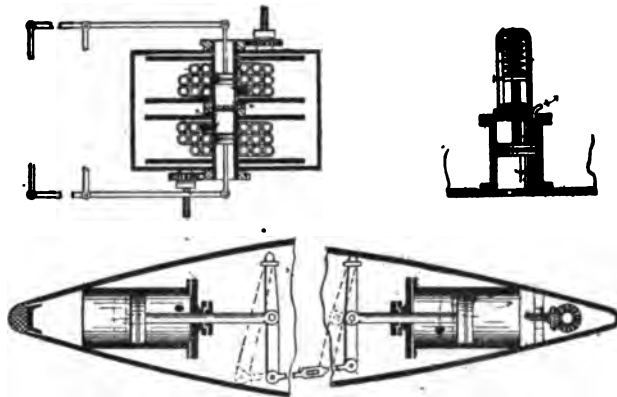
, 261 et 262 (Freese et Gawn, 1894).
